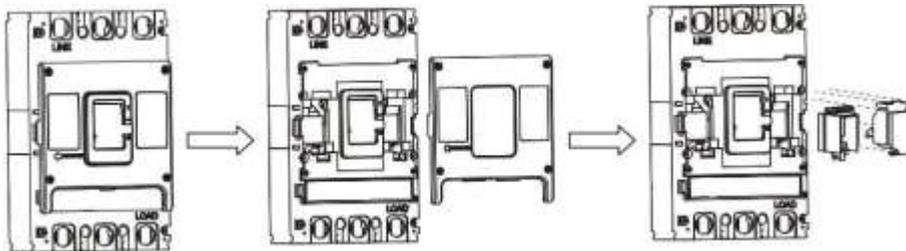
Схема установки аксессуаров внутрь корпуса аппарата
